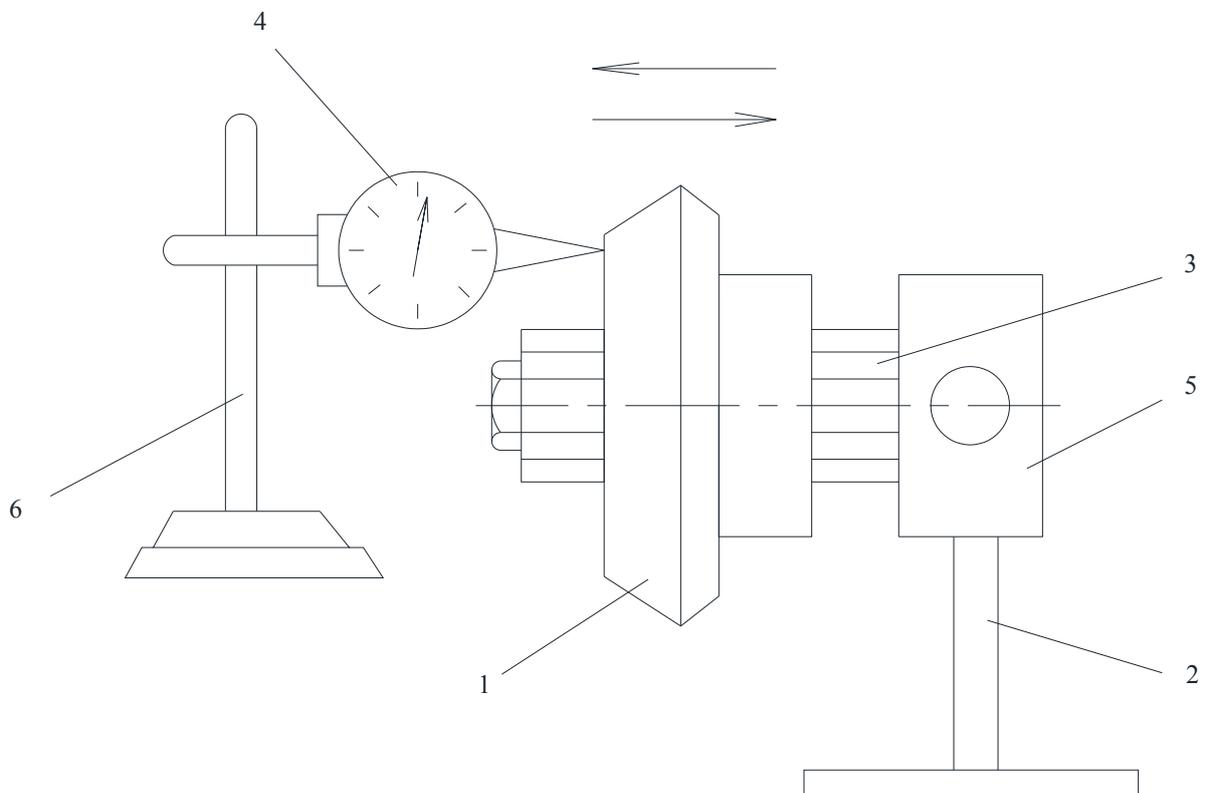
Схема контроля углового качания колеса на валу: 1 – зубчатое колесо; 2 – стойка; 3 – вал; 4 – индикатор; 5 – втулка; 6 – штатив
